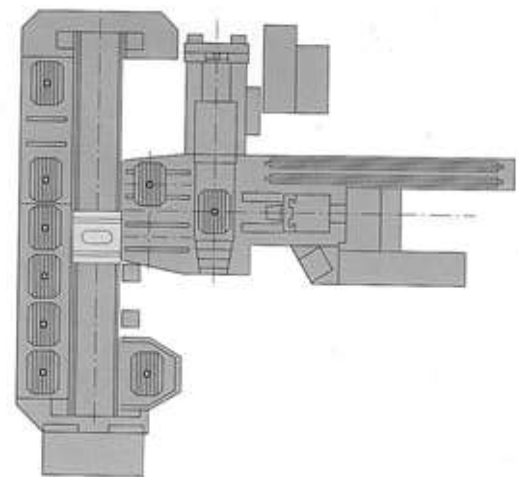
Компоновка ГВМ DECKEL DC55 (Німеччина) – з палетами для токарної обробки
